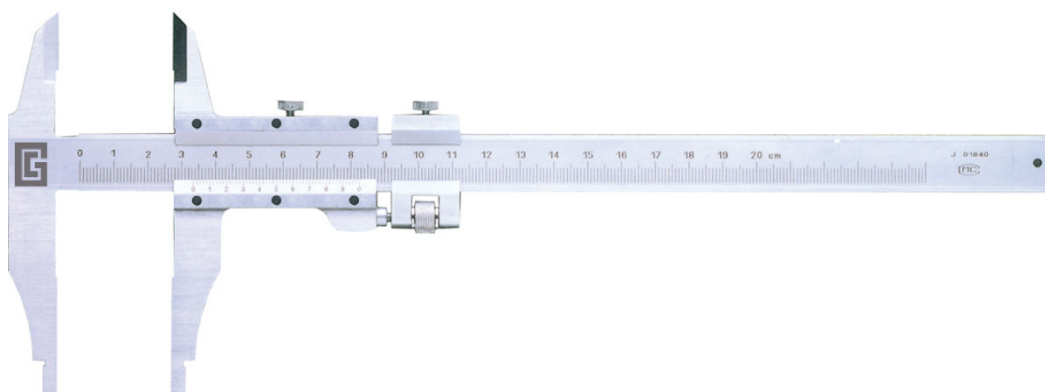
Общий вид штангенциркулей типа ШЦ-II.
